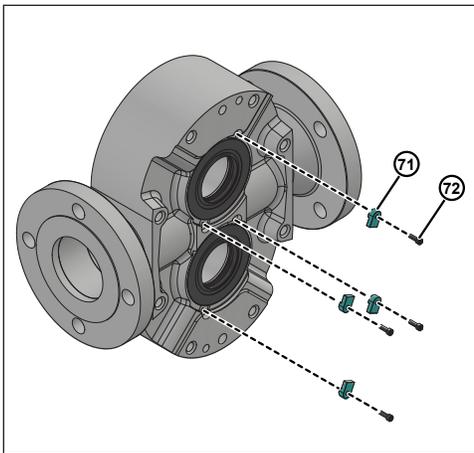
Schrauben und Aufnahmelasche montieren
